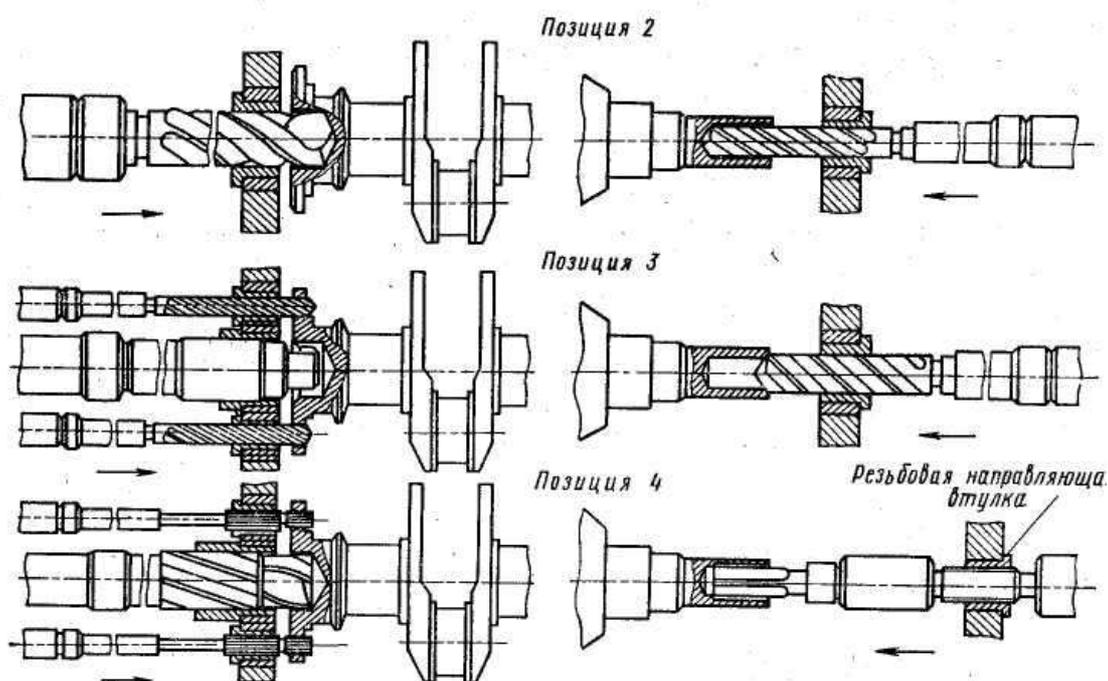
Схема наладки двустороннего шестипозиционного сверлильного станка для обработки отверстий в переднем и заднем концах коленчатого вала
